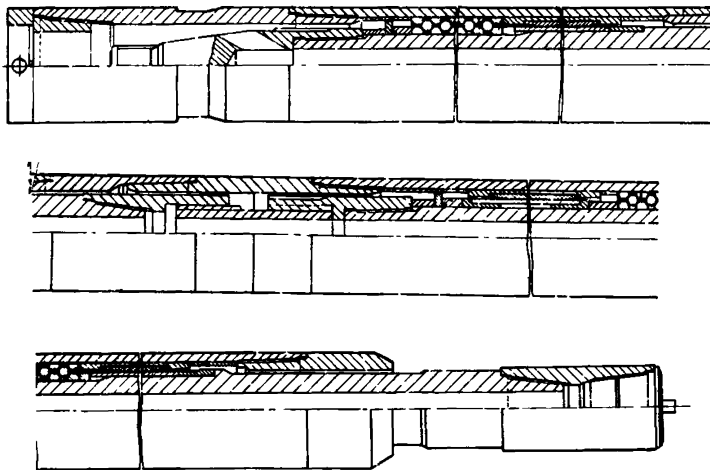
Шпиндель-отклонитель ШОГ-195 (сборочный чертеж).
